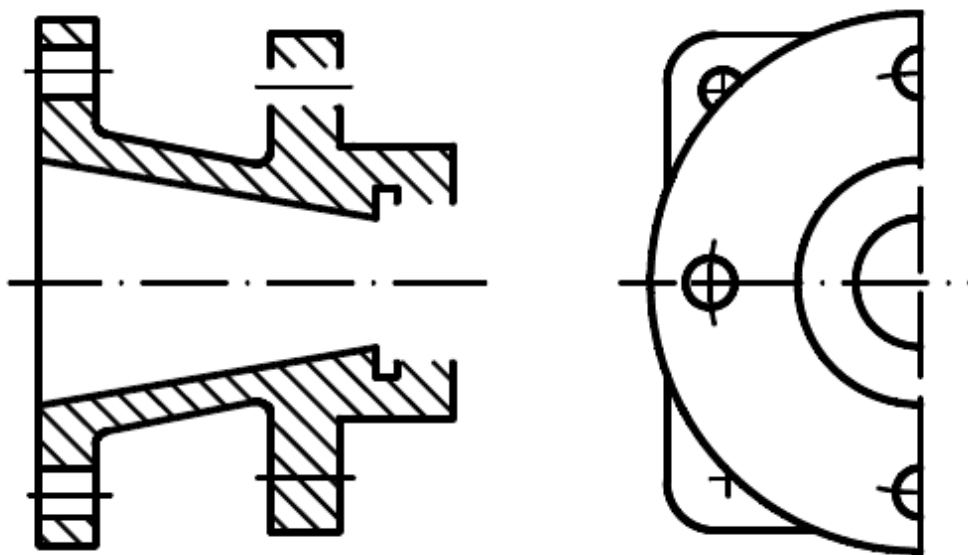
Первый этап выполнения рабочего чертежа детали по чертежу общего вида (деталирование)
